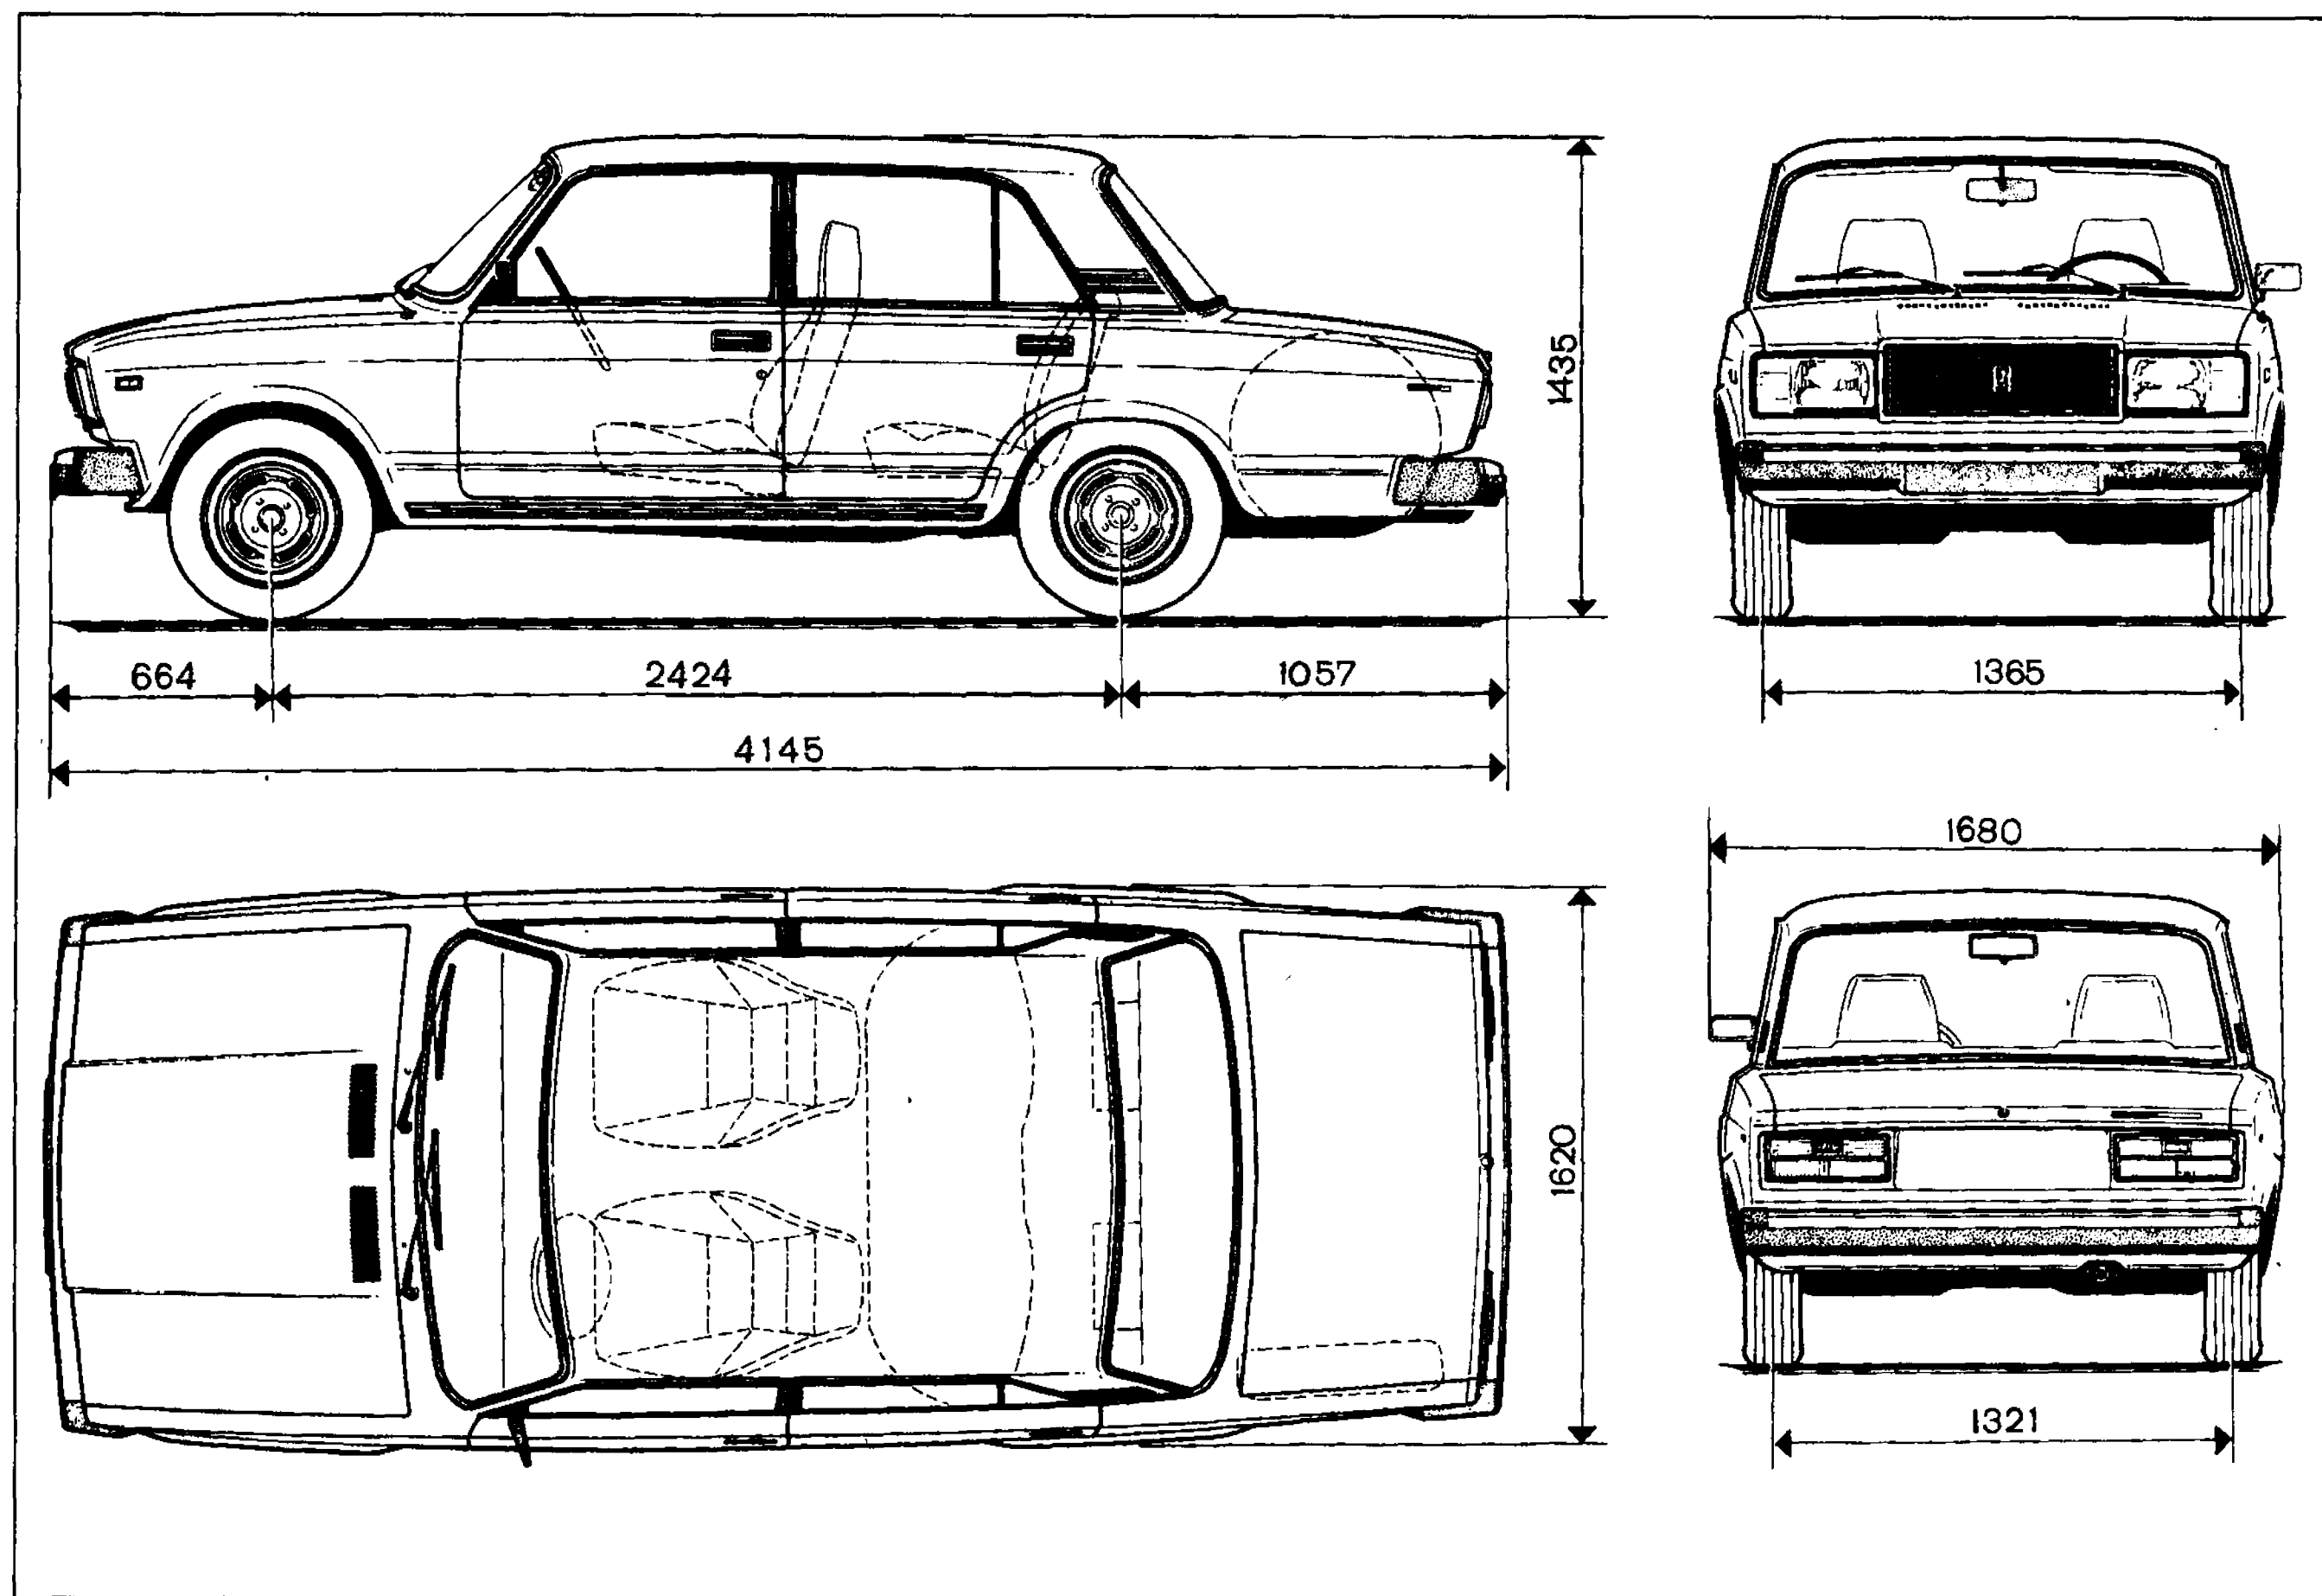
Габаритные размеры автомобиля ВАЗ-2107
